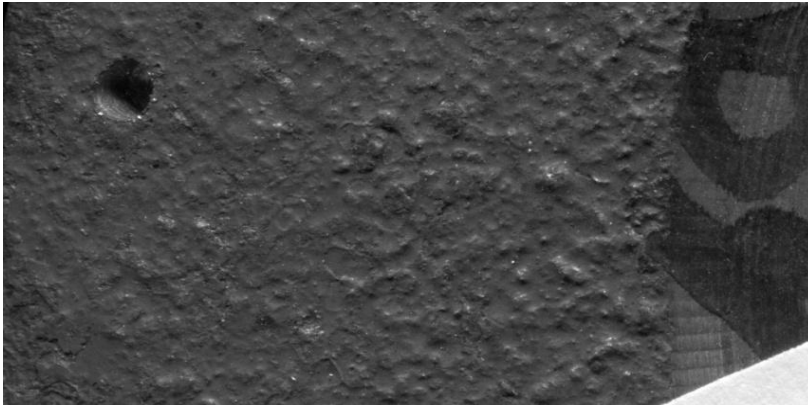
Необроблена внутрішня поверхня №18 корпусу водолічильника КВБ-10
